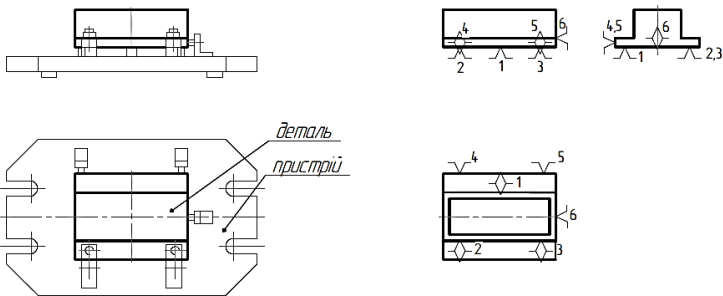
Схема базування корпусної деталі по площині основи і двох бокових поверхнях.
